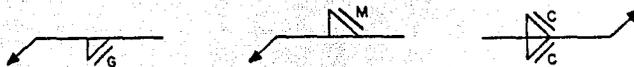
(cont.)— APLICACION DE SIMBOLOS DE SOLDADURA DE FILETE
